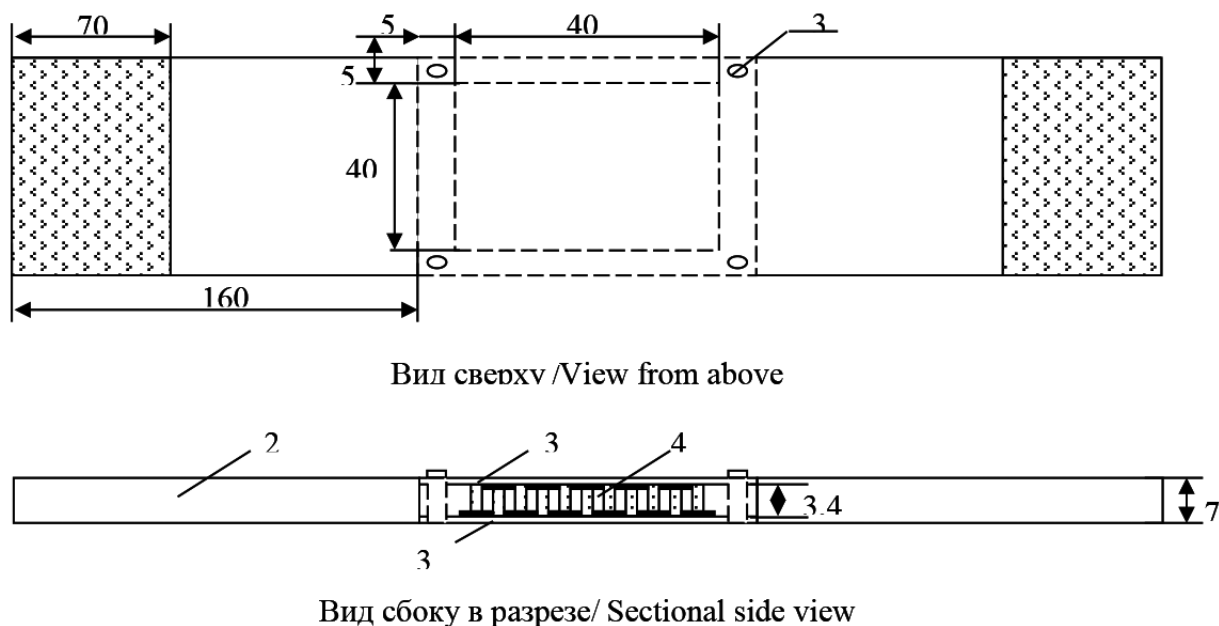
Эскизный рисунок лабораторного образца термоэлектрического устройства для остановки кровотечения с основными геометрическими размерами
